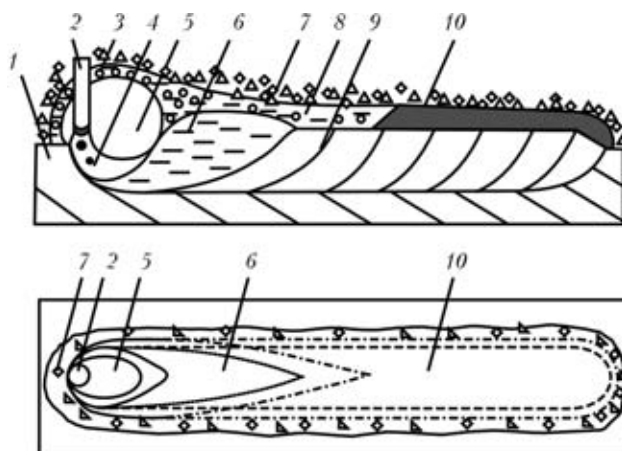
Схема процесса электродуговой сварки под флюсом согласно существующим представлениям: 1 — основной металл; 2 — электродная проволока; 3 — шлаковый пузырь; 4 — зона горения дуги; 5 — кратер; 6 — сварочная ванна; 7 — флюс; 8 — жидкий шлак; 9 — шов; 10 — шлаковая корка
